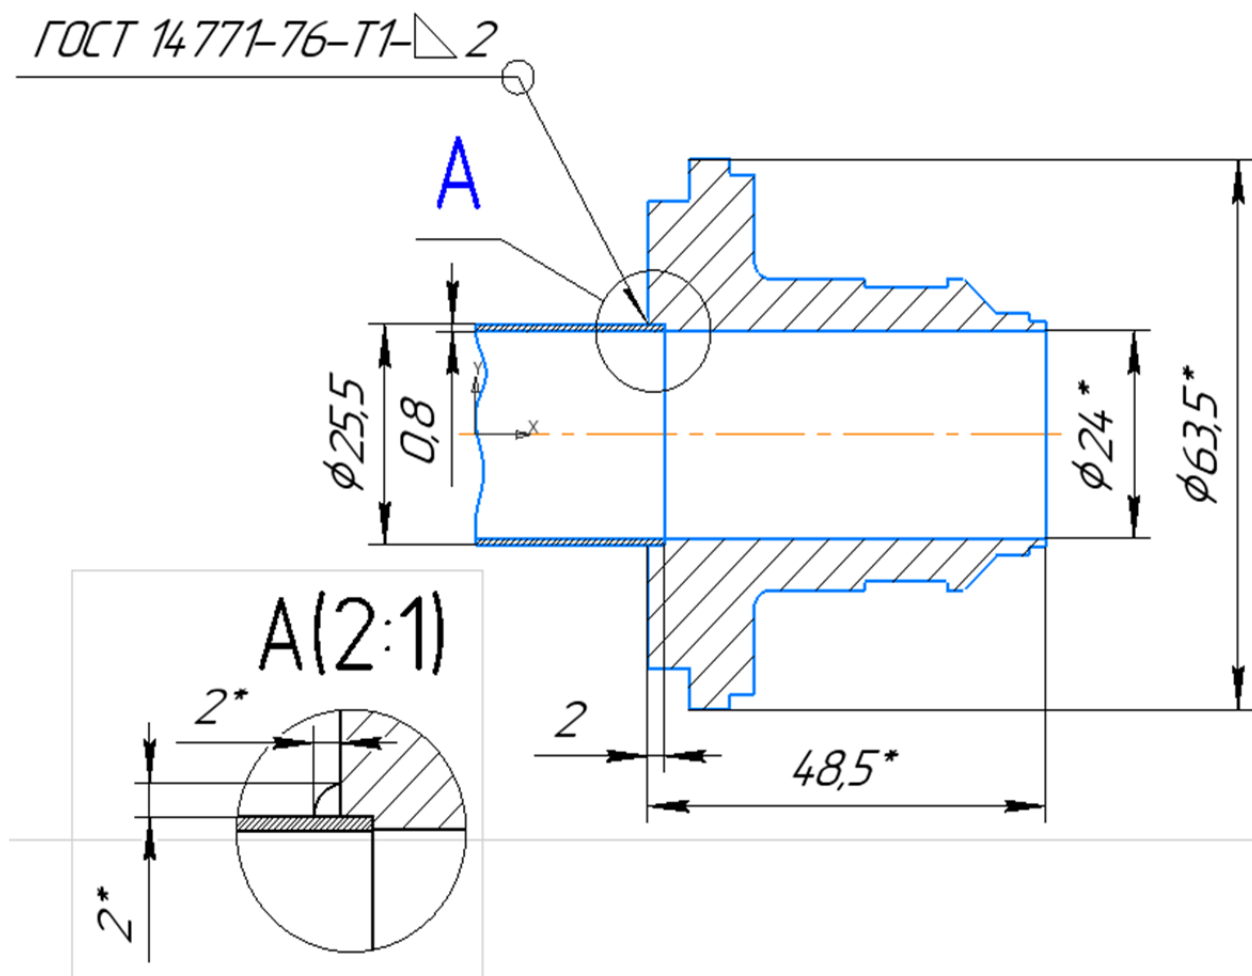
Основные геометрические размеры и конструктивные элементы свариваемых деталей
